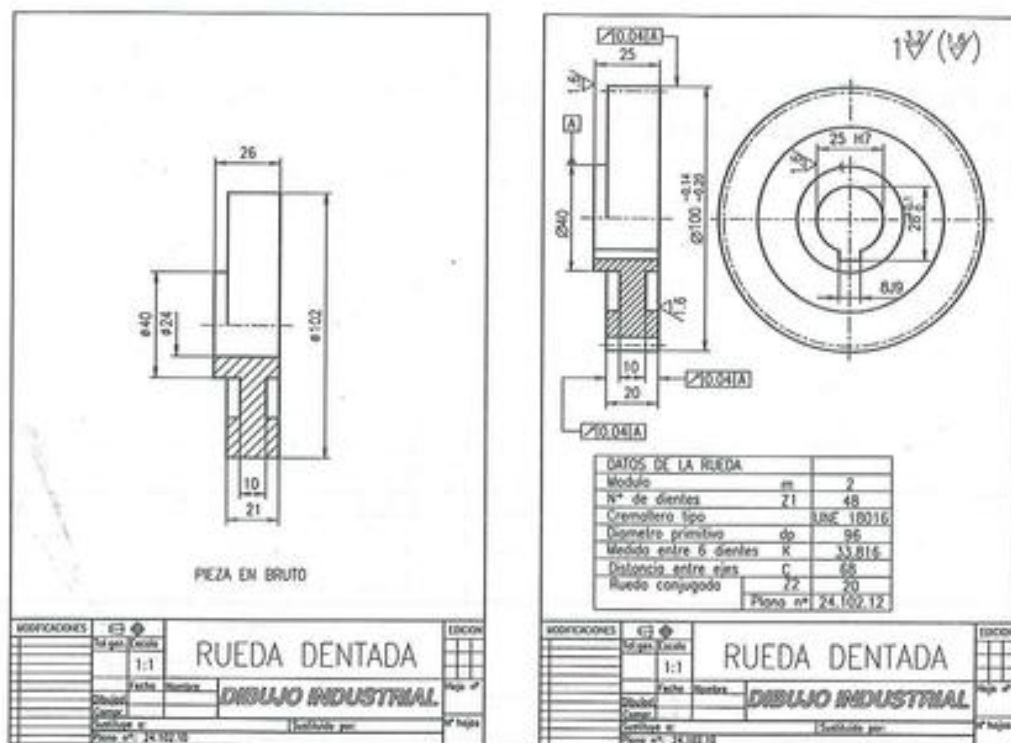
Dibujo de despiece. Plano de pieza en bruto (Izq.). Plano de pieza terminada (Dcha.).
